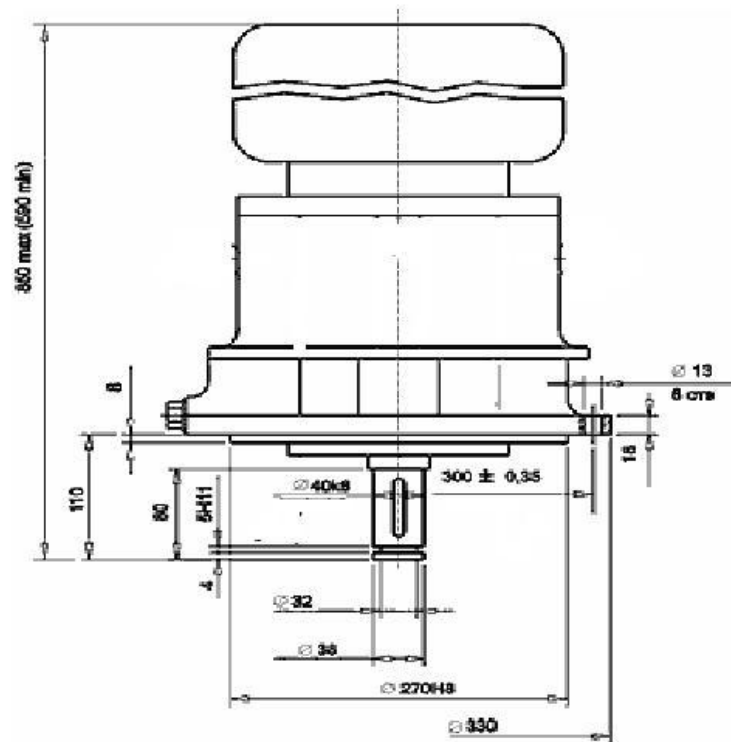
Зовнішній вигляд і габаритні розміри редуктора МПО1М
